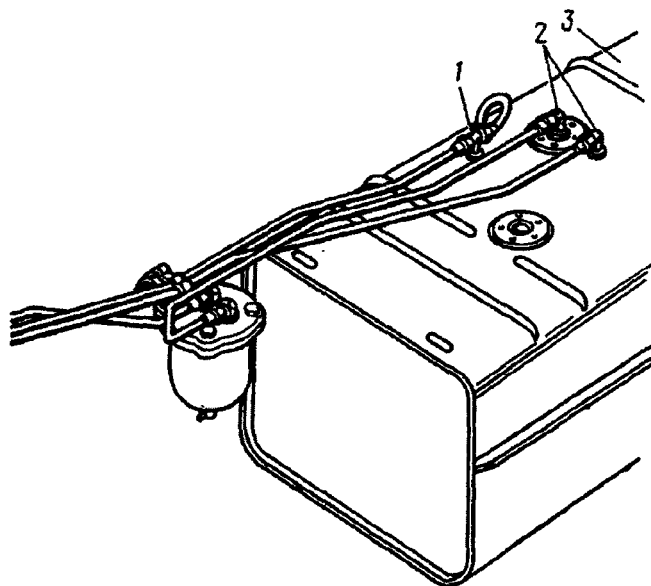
Установка топливного бака на автомобиле КамАЗ-43105:
